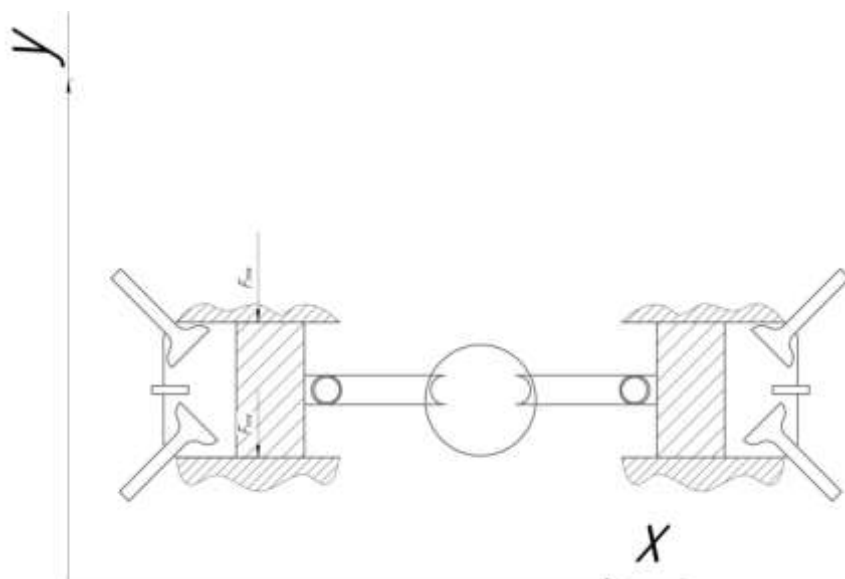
Поршни в блоке оппозитионного двигателя
